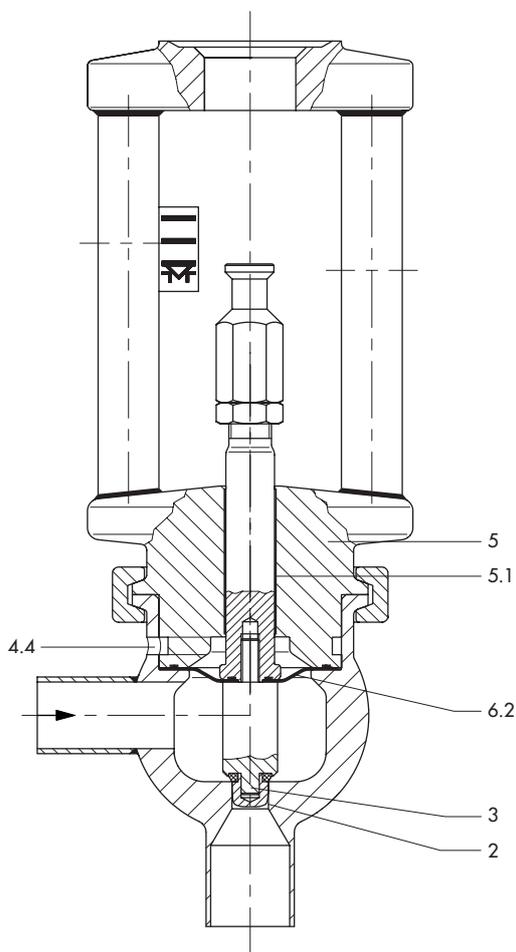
· Угловой клапан тип 3249 в стандартном исполнении
